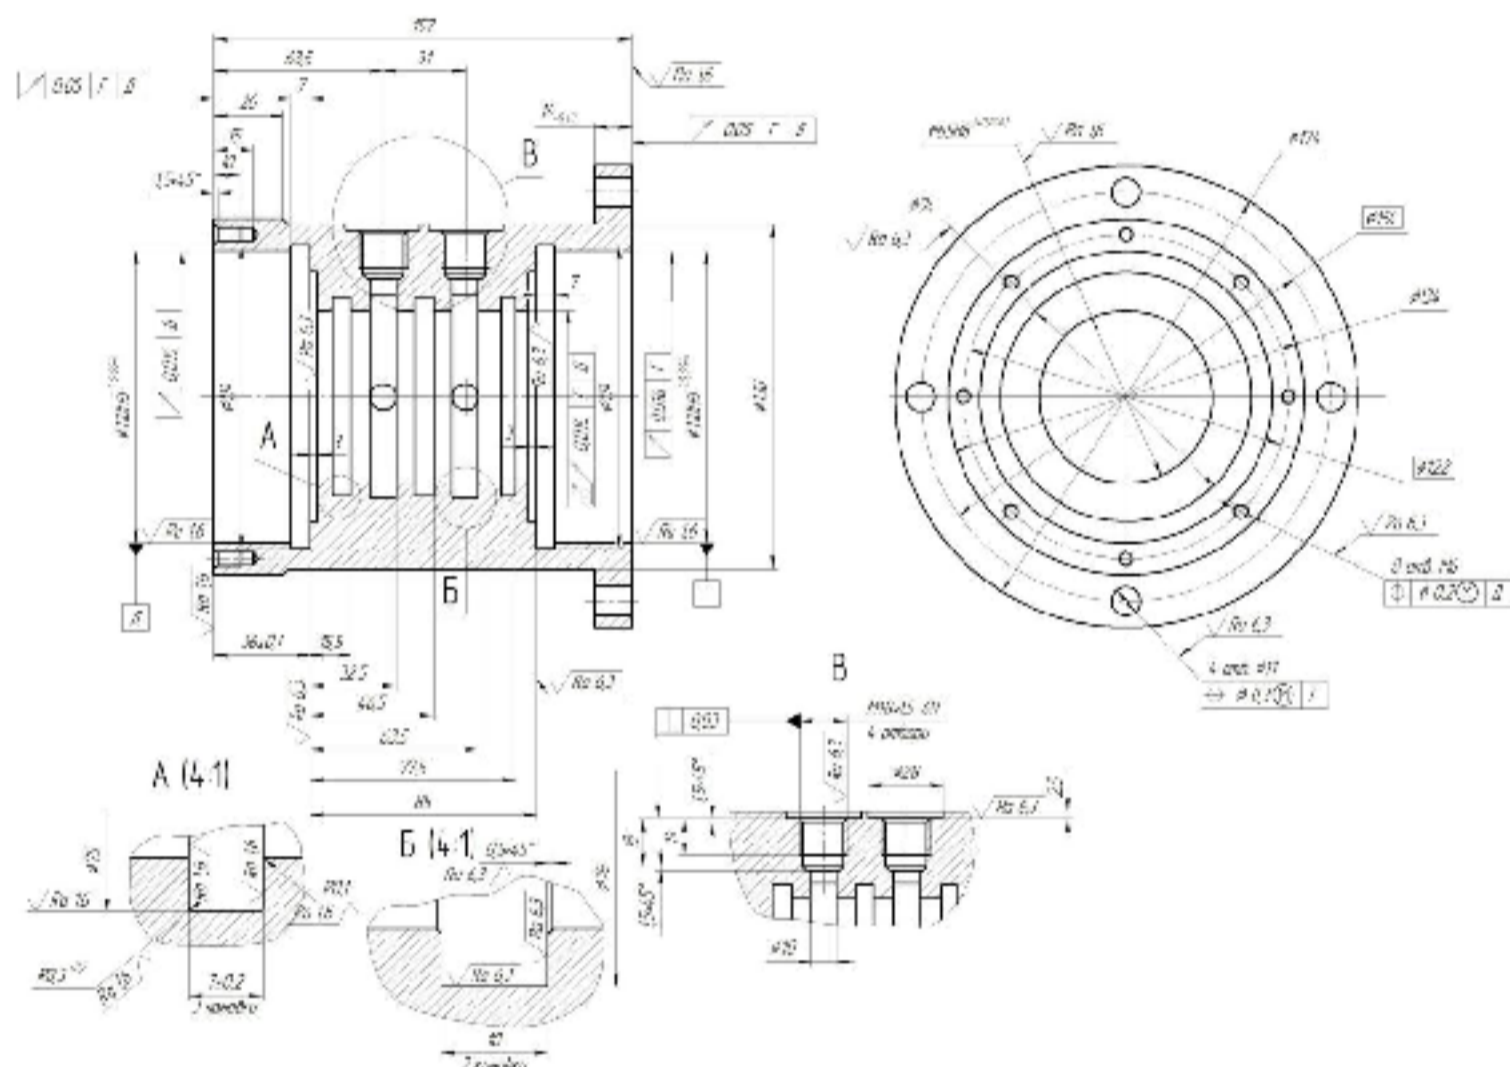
Ескіз деталі «Корпус гідромуфти 12.00.001»
